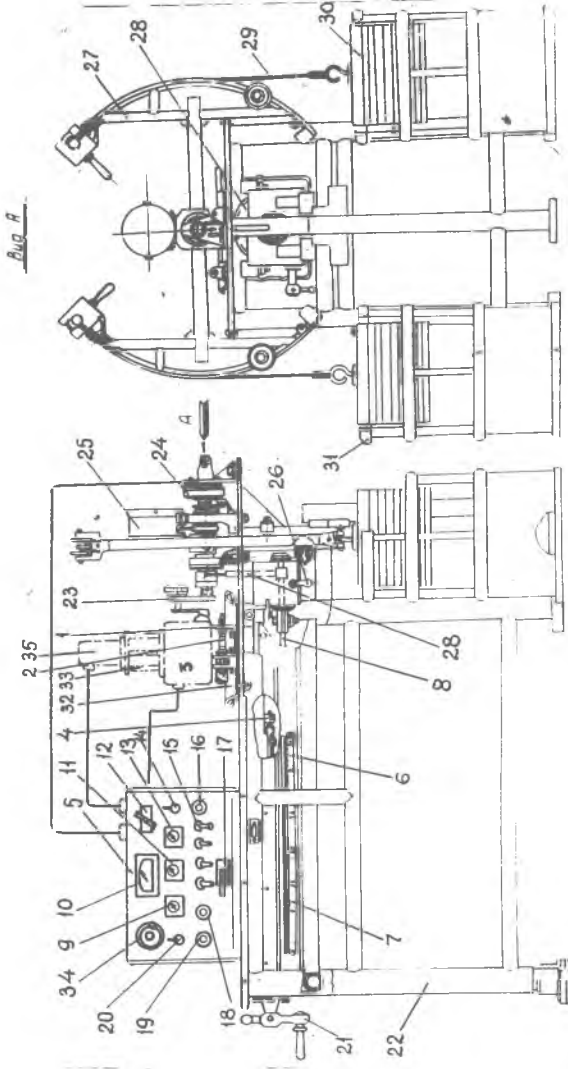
Общий вид установки для регулировки и контроля параметров рулевой машины
